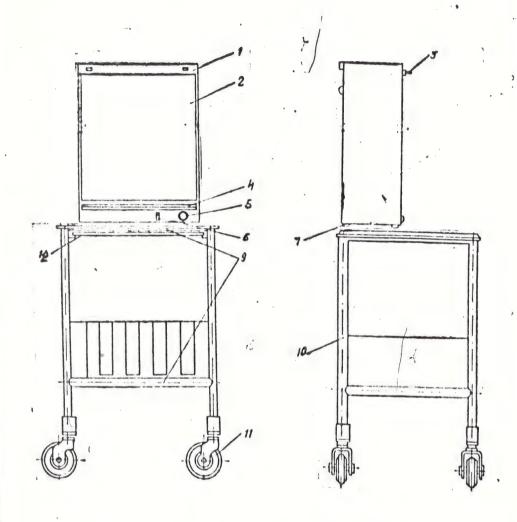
Петатоской общего назначения передвижной ПТ-48. Общий вид 1— корпус; 2— экран; 3— кронштейн; 4— лоток; 5— ручка регулировки пркости; 6— выключатель; 7— ножка; 9— полка; 10— каркас; 11— колесо; 12— полка бывышмая
